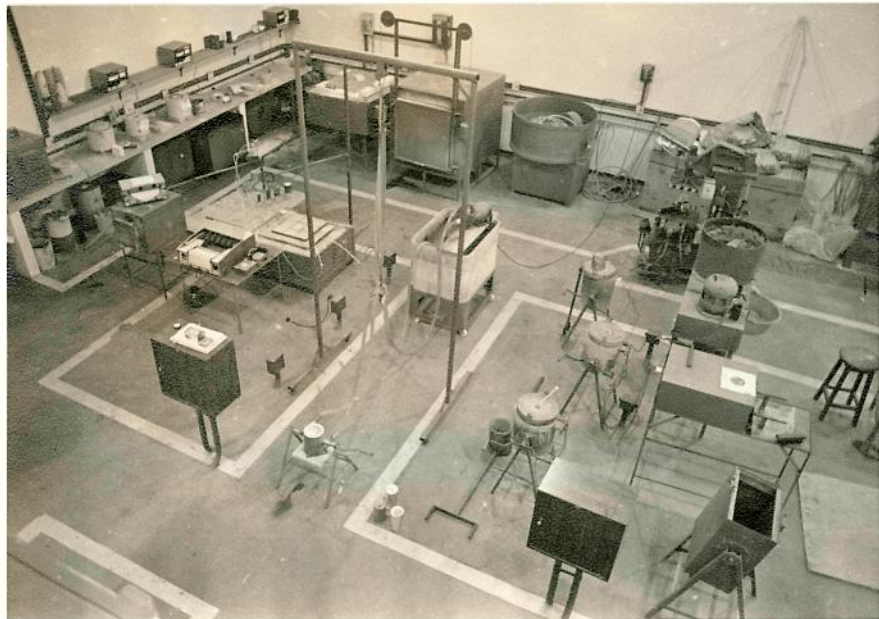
" SISTEMA MOLDE INTERNO "
